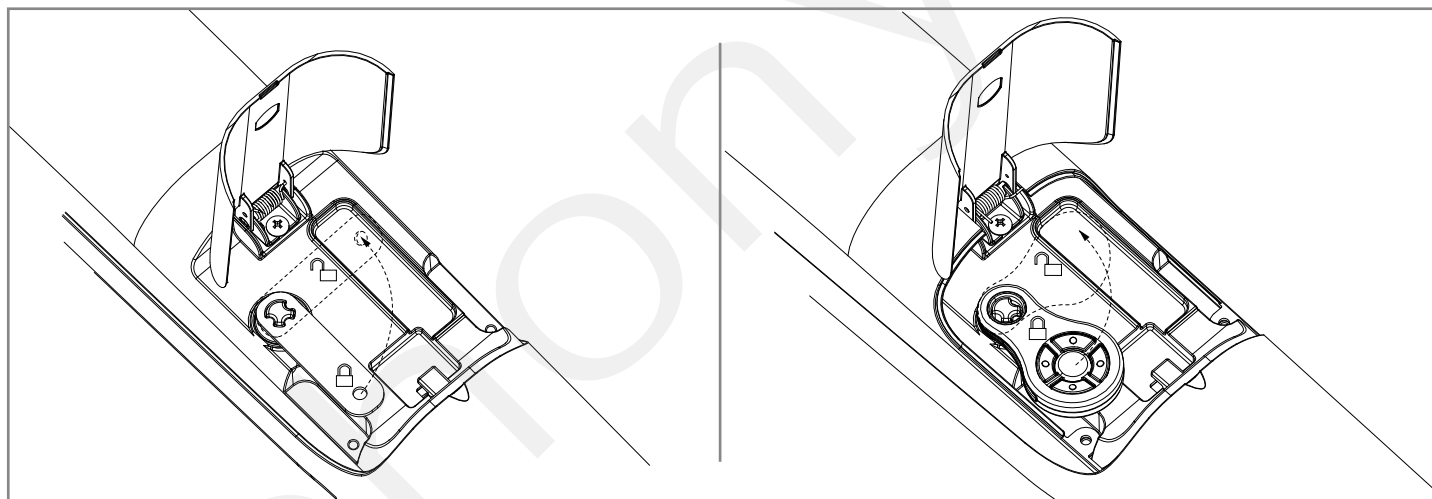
CZ - Zajištění převodového motoru a zadní konzoly
